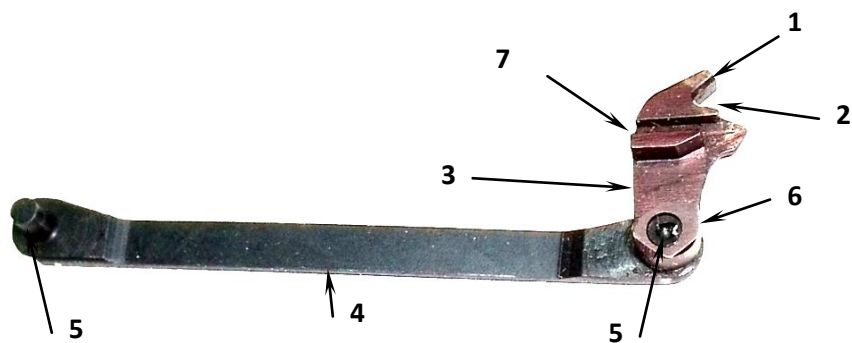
Устройство спусковой тяги с рычагом взвода
